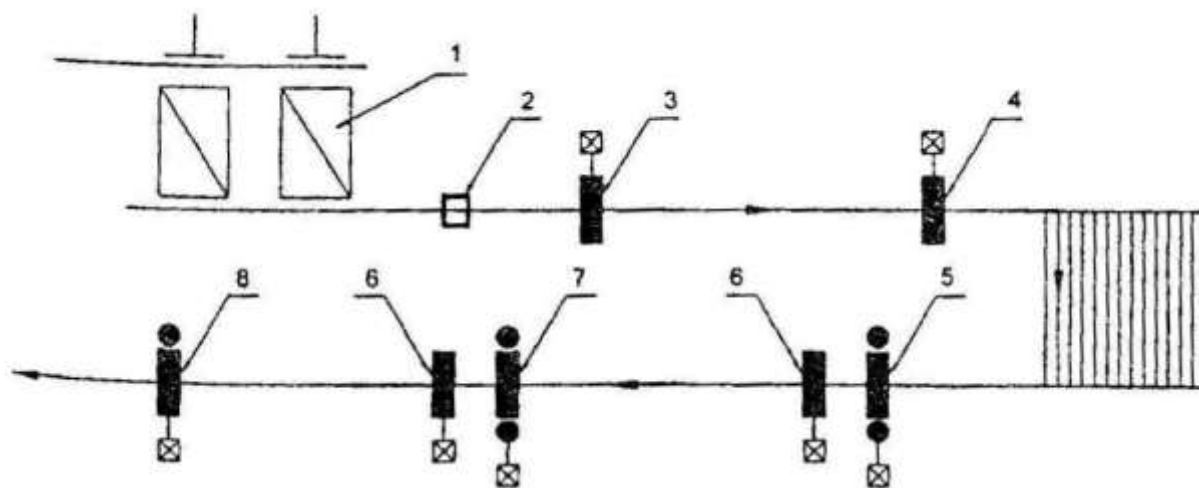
Схема калибровки для прокатки рельсов на заводе
